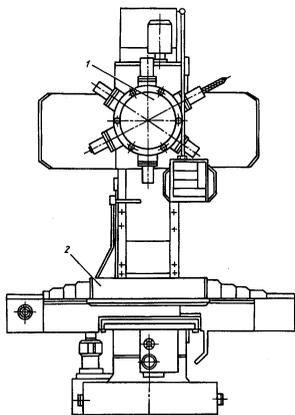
Общий вид вертикально-сверлильного станка с ЧПУ мод. 2Р135Ф2: 1 – шестипозиционная револьверная головка; 2 – крестовый стол
